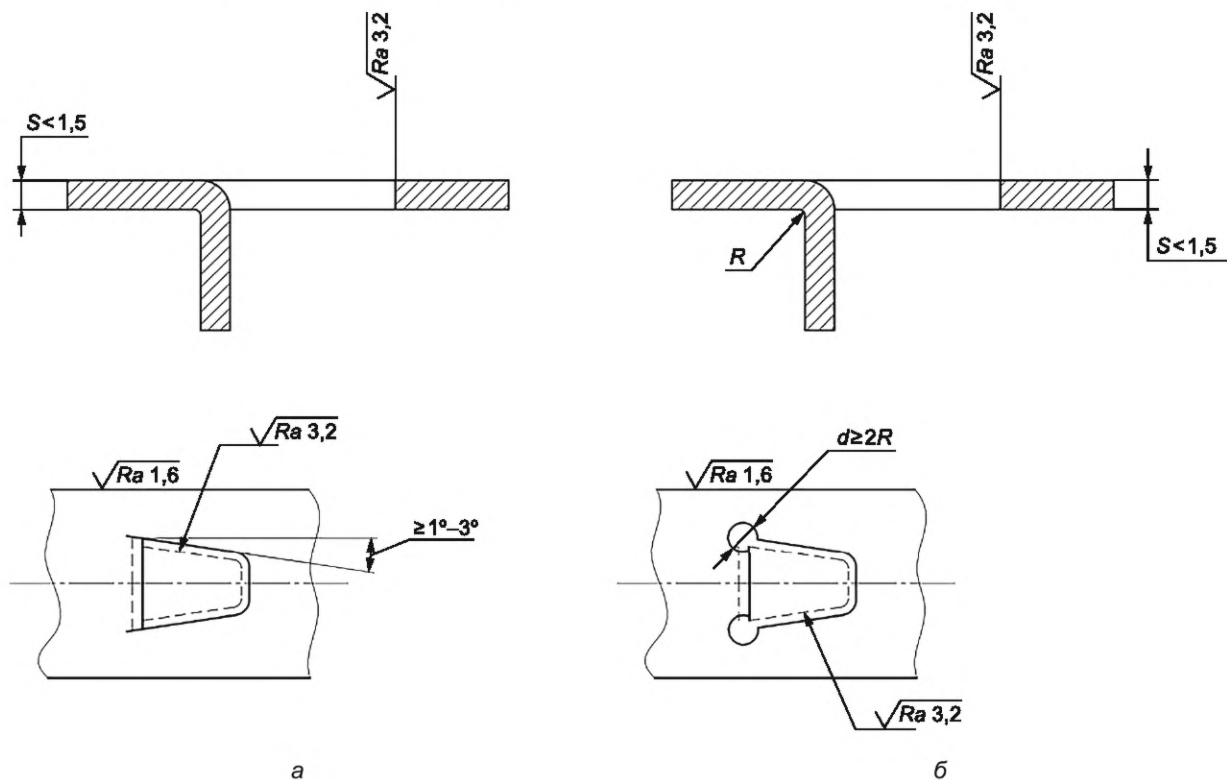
Обозначение параметров зубчатого элемента конструкции детали
